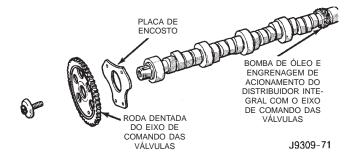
Conjunto do Eixo de Comando de Válvulas e Roda Dentada
